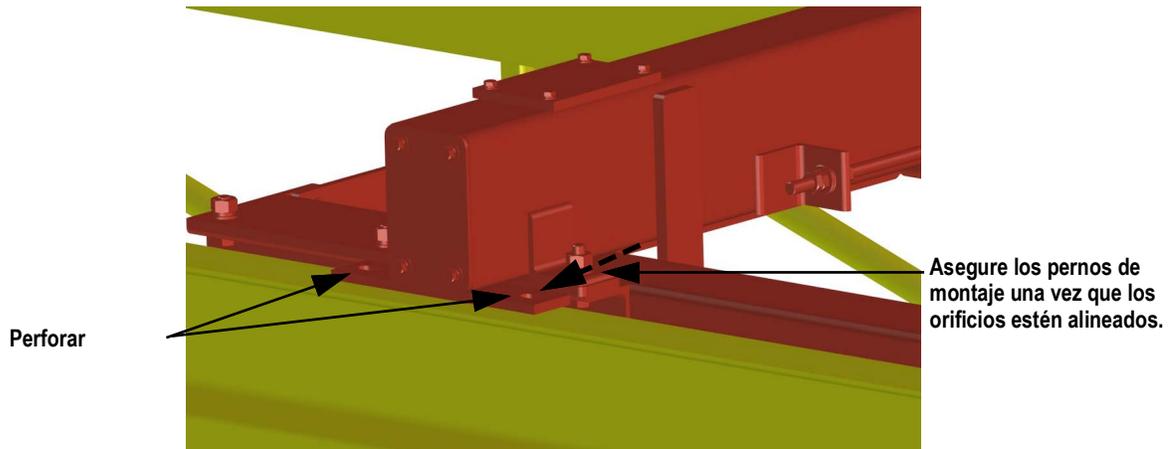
Utilice pernos para colocar el elemento de soldadura
